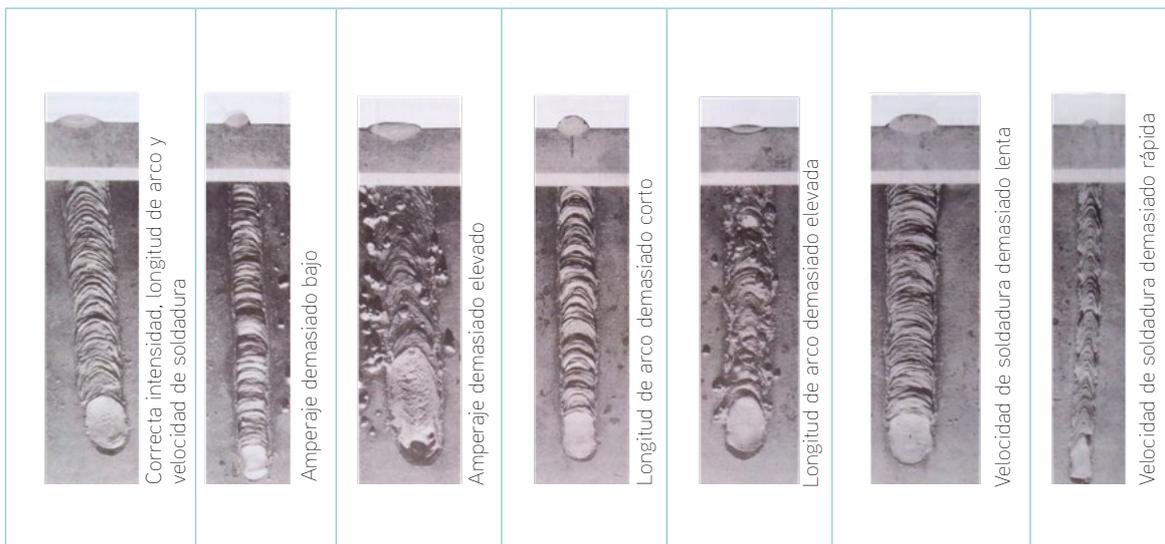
Efecto sobre el cordón de soldadura, de la intensidad, longitud de arco y velocidad de soldadura
